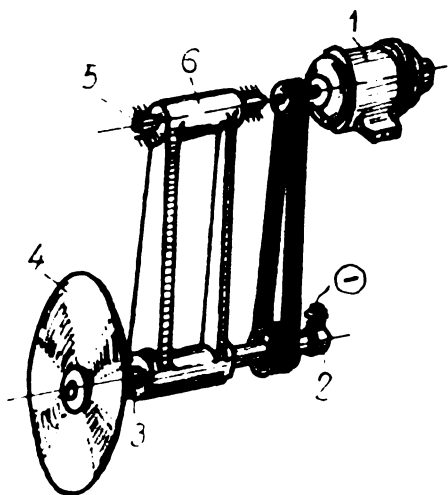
Acționarea principală la mașini de tăiere pentru produse până la 150 mm: 1-motorul electric; 2-inel colector de curent; 3-arbore; 4-discul; 5-axe de pendulare; 6-corpul dispozitivului de pendulare
